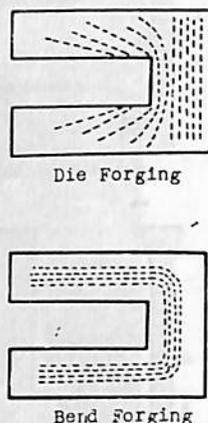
Die Forging と Bend Forging のゴースト露出の傾向の比較
